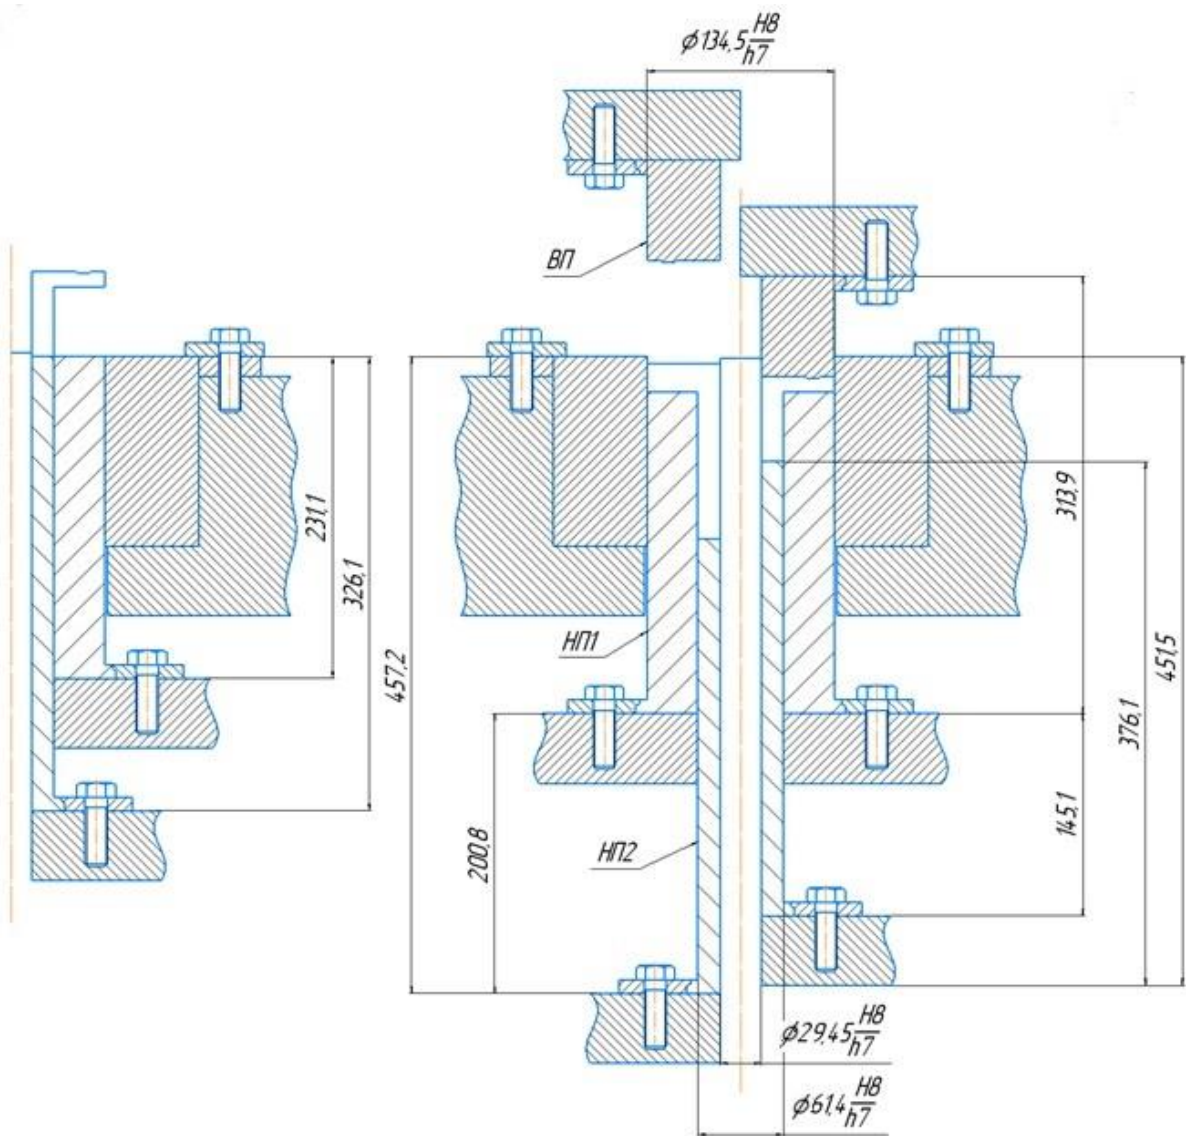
Пресс-форма для прессования внешних фланцев (схема выпрессовки, засыпка и прессовка)
